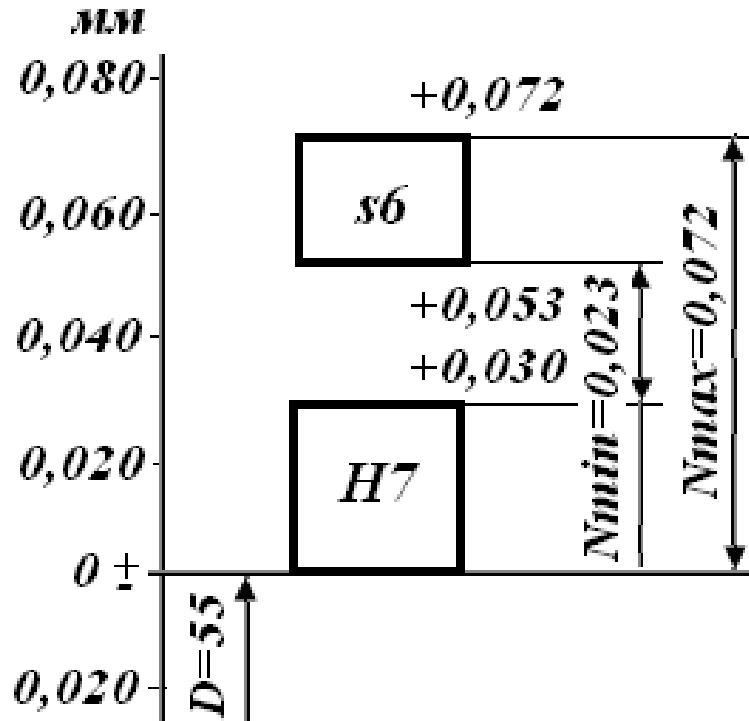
Схема розташування полів допусків деталей з'єднання  $\varnothing 55H7/s6$
